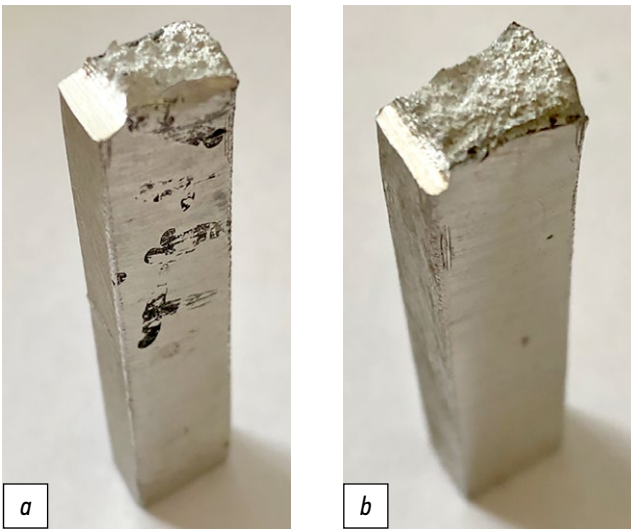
Разрушенные образцы после испытания на ударную вязкость: а — 6082Т сваренный с напечатанным алюминием; б — АМг5, сваренный с напечатанным алюминием.
